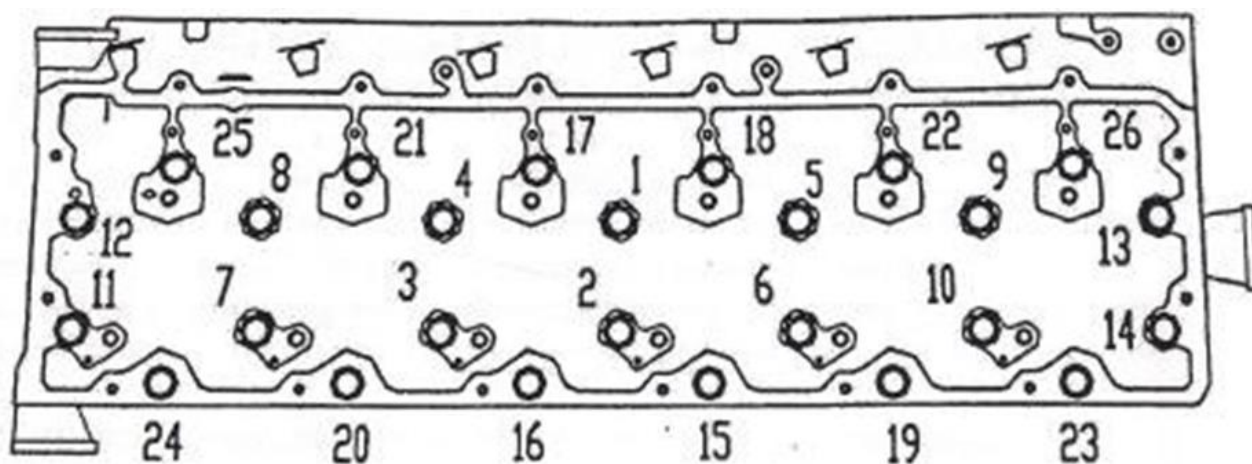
Порядок затяжки болтов крепления головок цилиндров двигателей ЯМЗ-536 (обязателен для каждого приёма затяжки)
